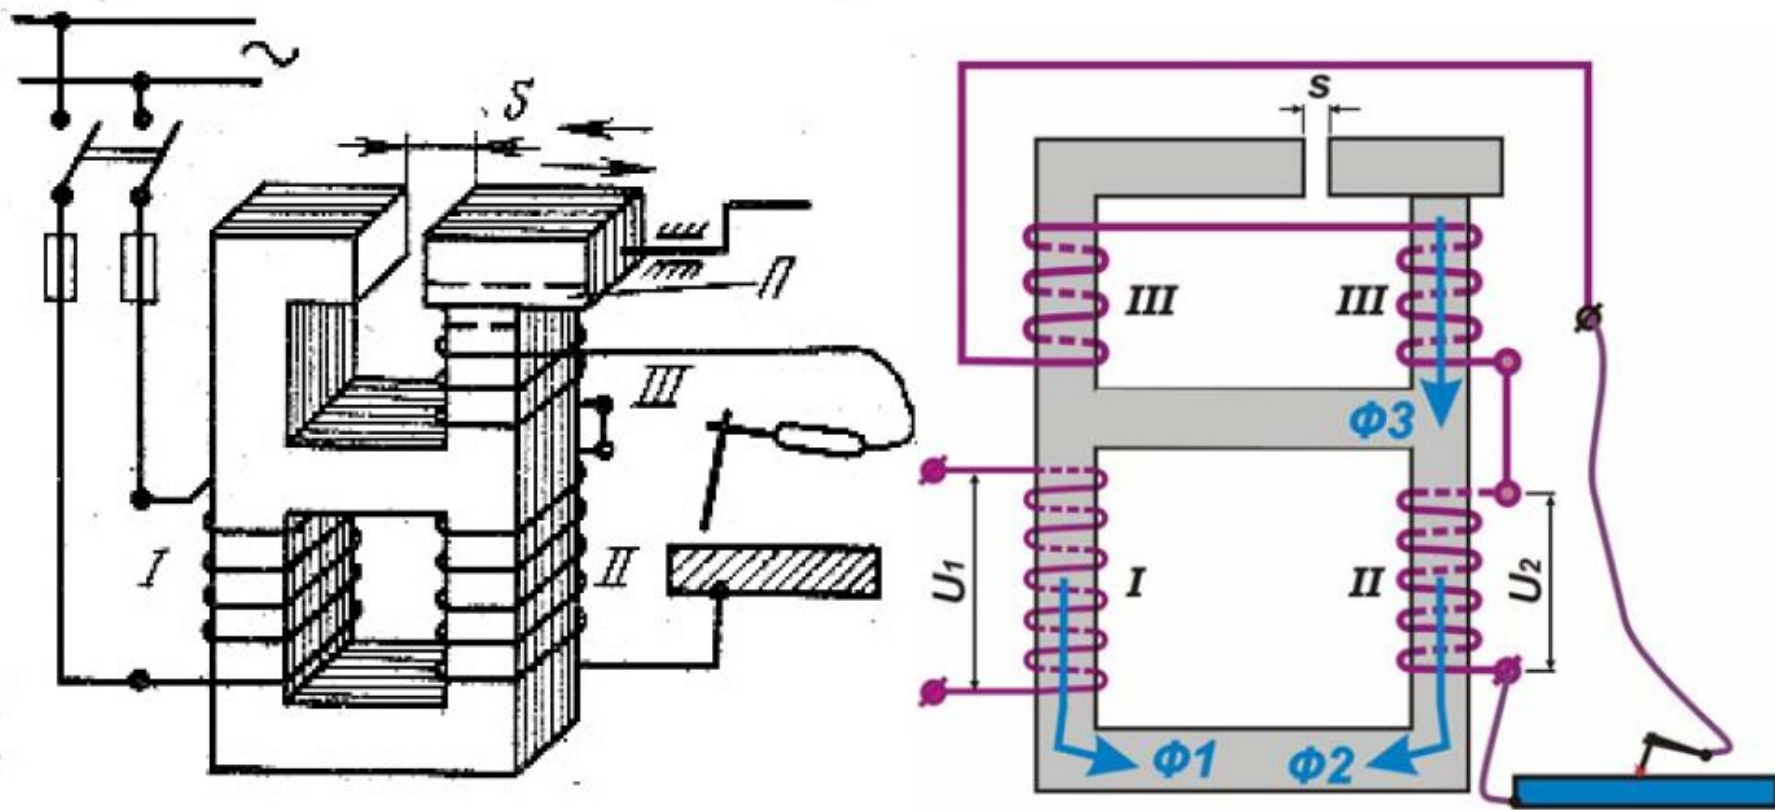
Схема сварочного трансформатора типа СТН
